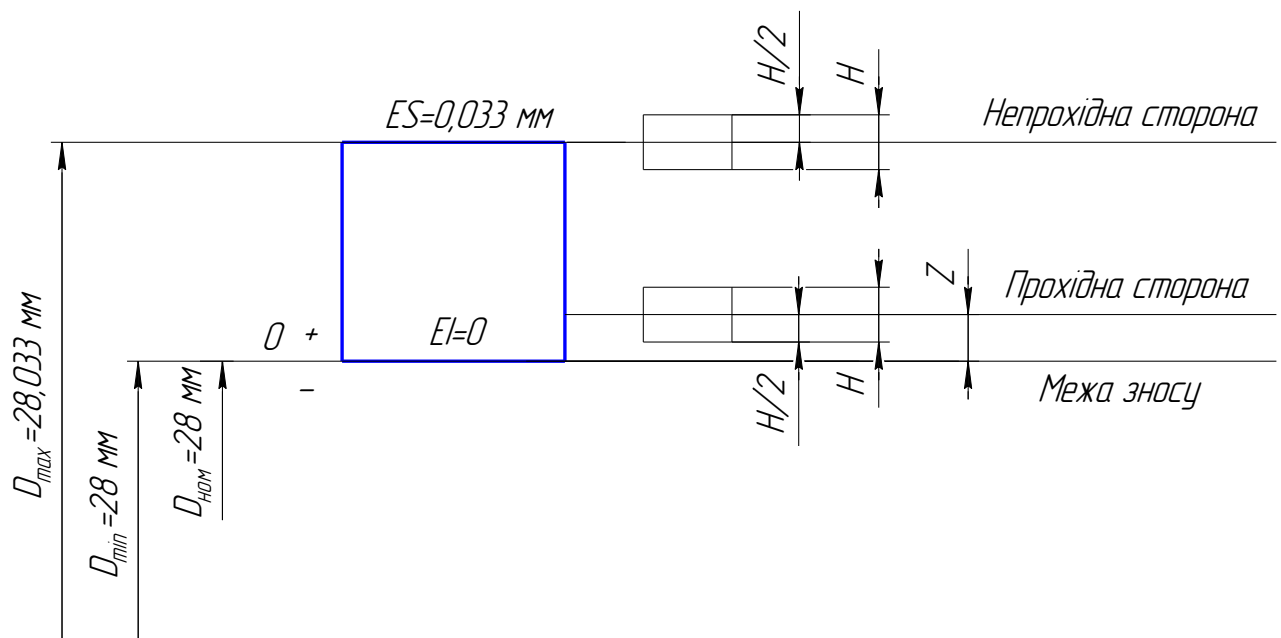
Схема розташування допусків робочих поверхонь калібрів для контролю розміра $\varnothing 28H8^{(+0,033)}$
